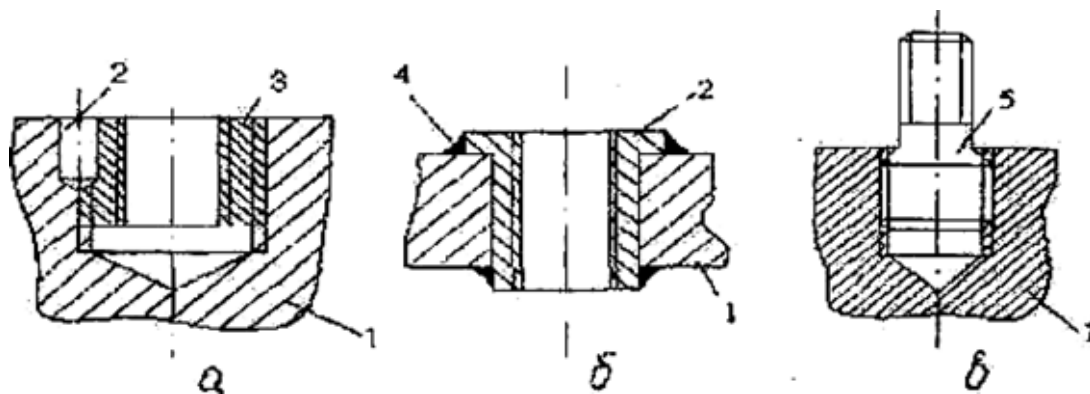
Ремонт резьбы: *а* и *б* - установкой резьбовой и приварной втулки; *в* - нарезанием резьбы увеличенного размера; 1 - корпус; 2 - стопорный штифт или винт; 3 - втулка; 4 - сварной шов; 5 - ступенчатая шпилька
